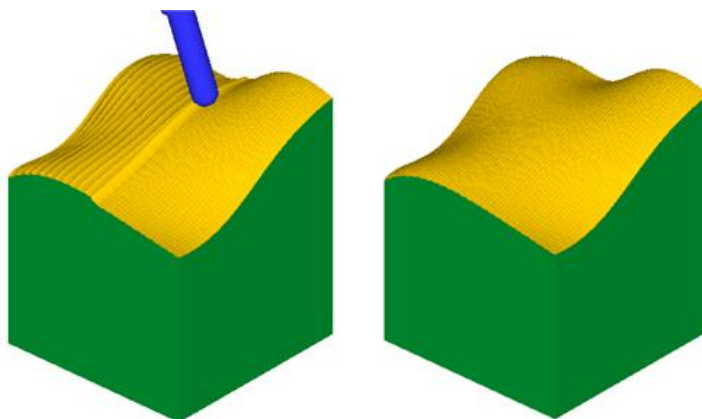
Vzhled obrobku při operaci hrubování obecné plochy
